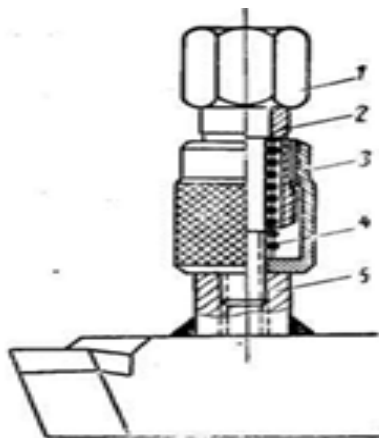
Гаситель ударного действия 1 – сердечник; 2 – втулка; 3 – крышка; 4 – разжимающая пружина; 5 – переходная гайка
